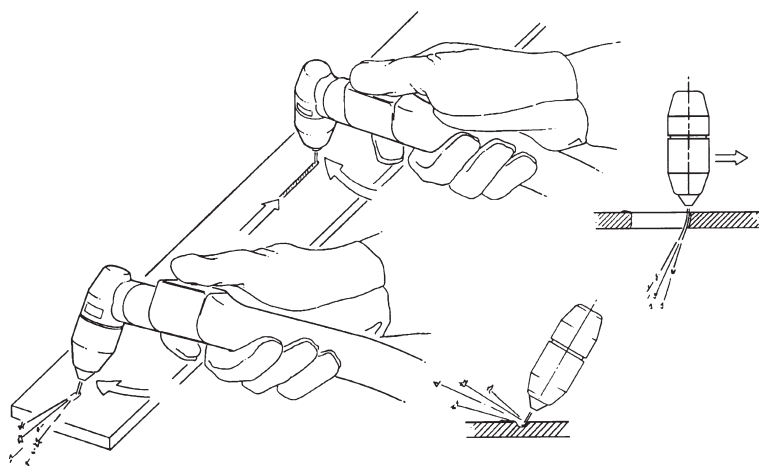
Прошивочный и режущий способы использования РТ-32ЕН
